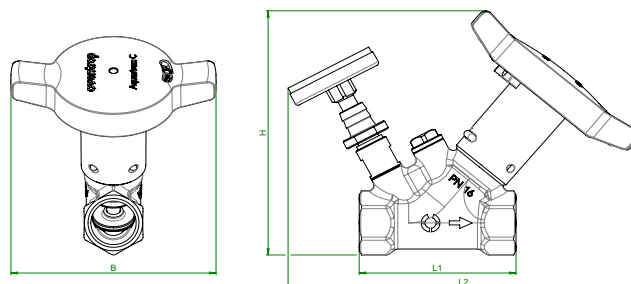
Abmessungen Seitenansicht / Frontansicht Innengewinde
